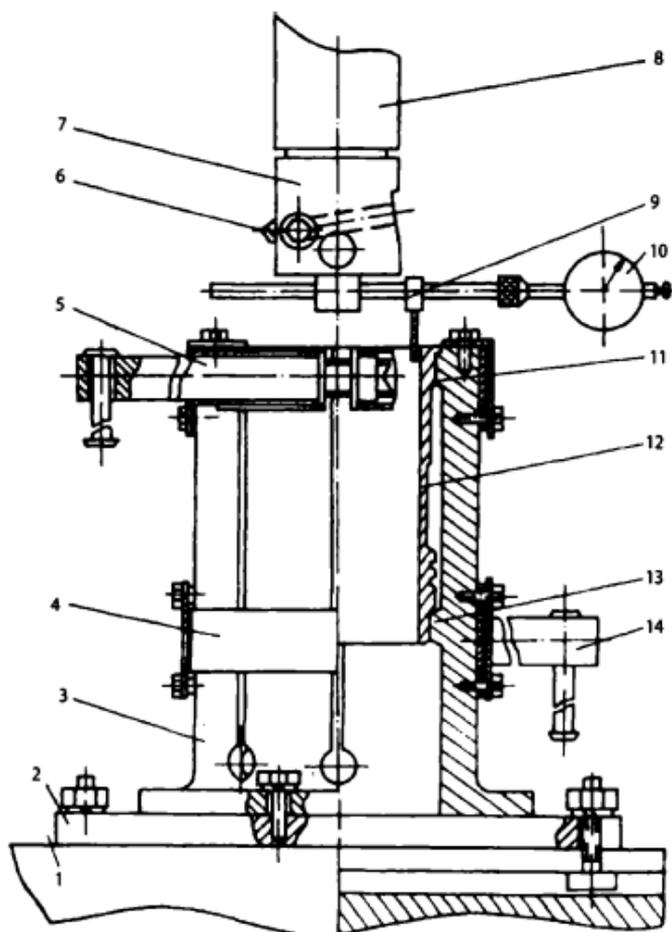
Пристосування для центрування і закріплення гільзи на столі розточувального верстата конструкції Є. Алешкіна
